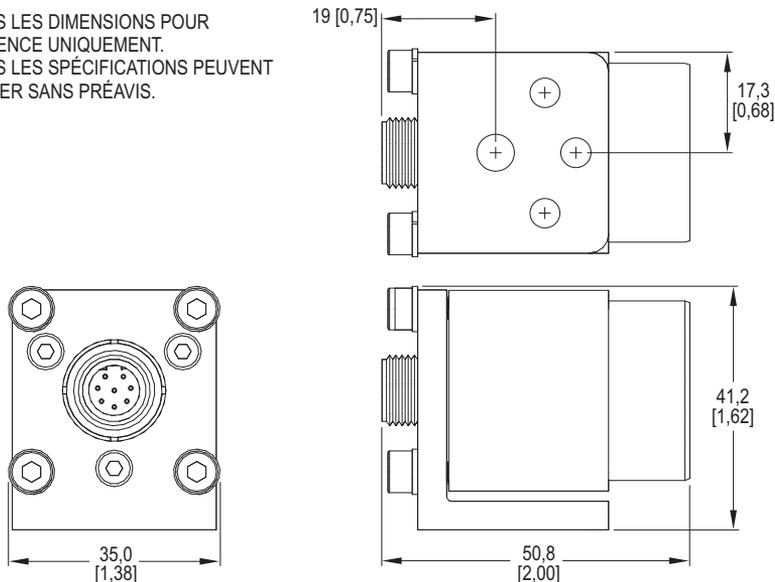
Dimensions de la monture de caméra déportée In-Sight
